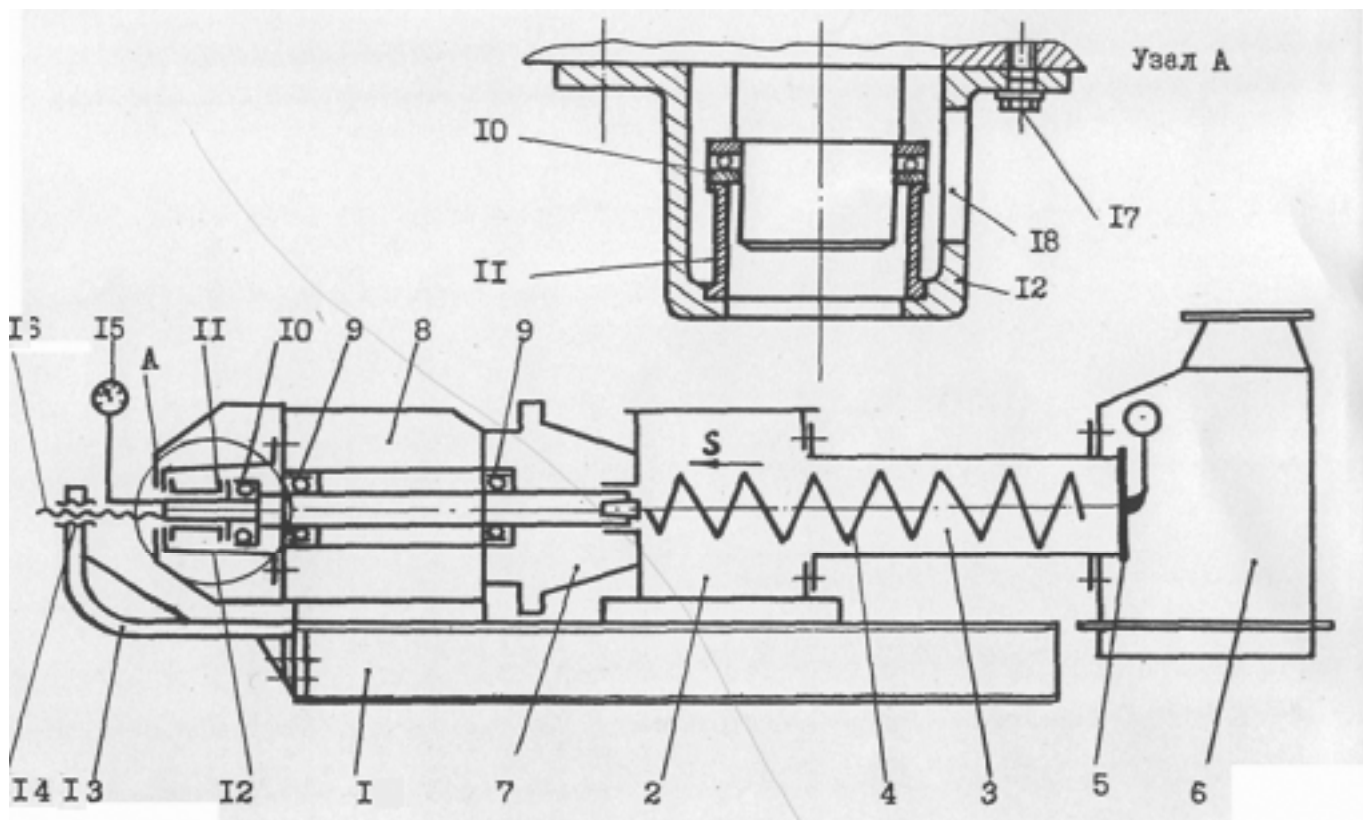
Схема установки датчика ДНП на пневмовинтовом подъемнике.
